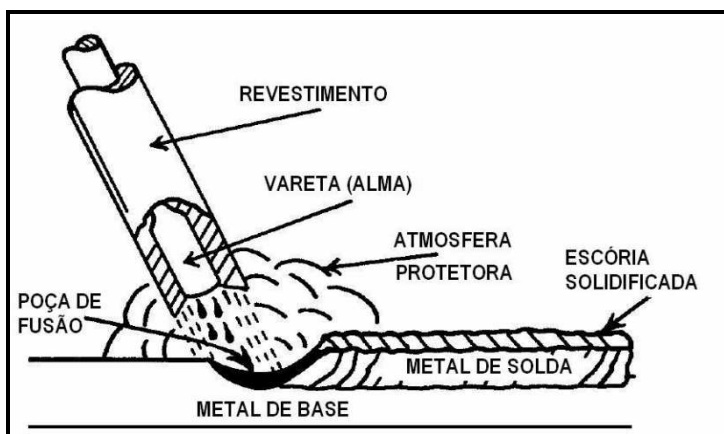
SOLDAGEM A ARCO ELÉTRICO COM ELETRODO REVESTIDO
